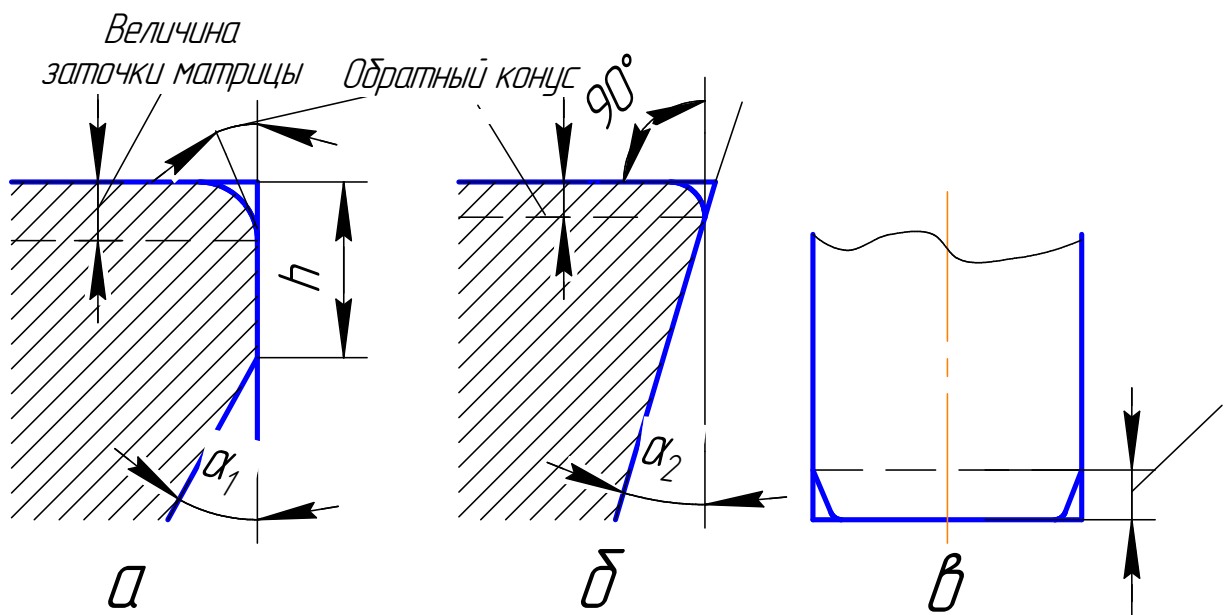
Зворотний конус і величина заточування при затупленні матриці і пуансона: а - матриці з циліндричним пояском; б - у матриці з конусом; в - у пуансона.
